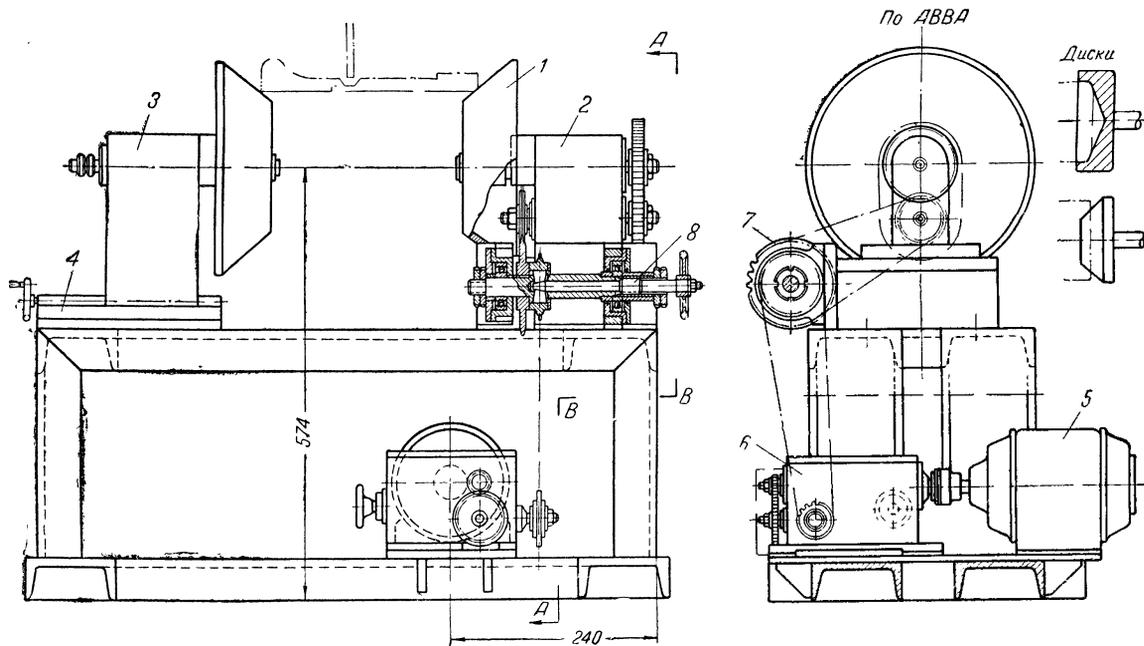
Приспособление для сварки вилки шасси.
